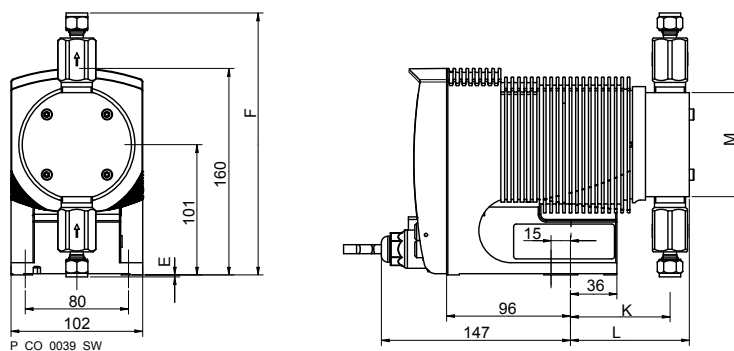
Габаритный чертеж Concept L, материал SST - размеры в мм
